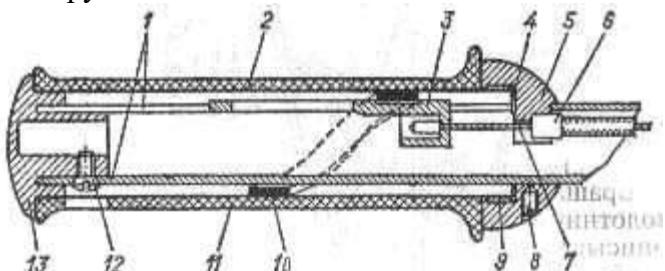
Разрез вращающейся рукоятки газа карбюраторов серии СБД (вид спереди):
